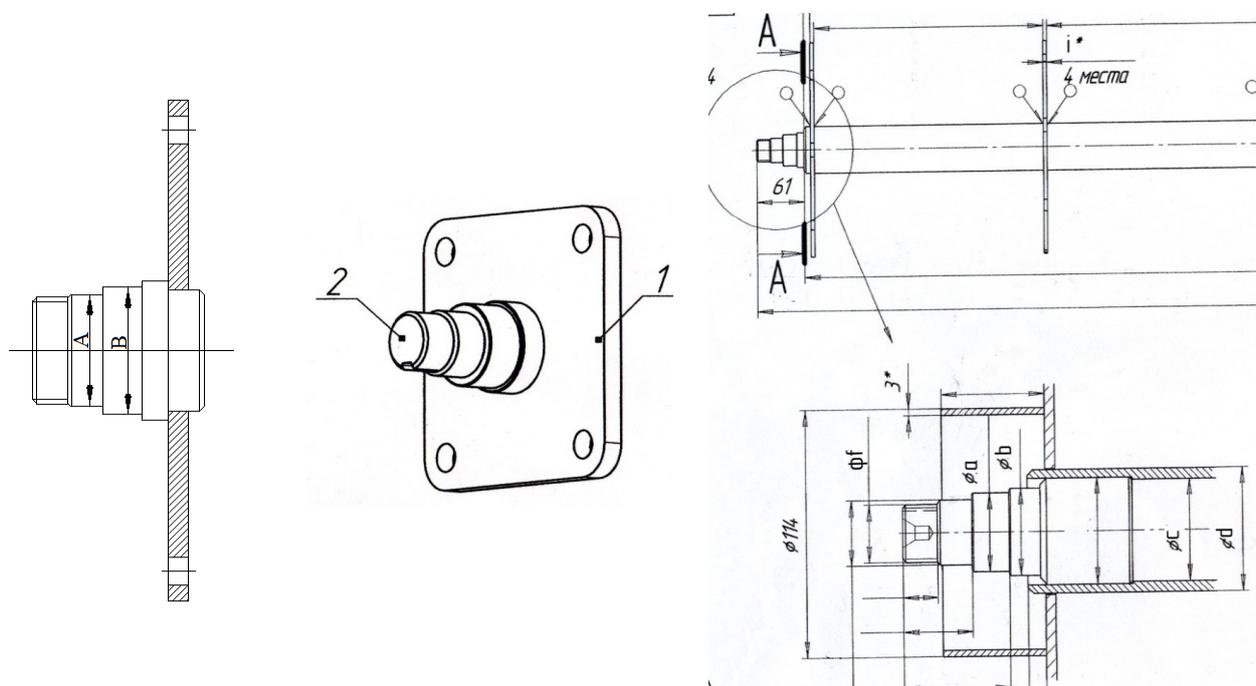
Схема сменной цапфы вала прикатывающего катка
